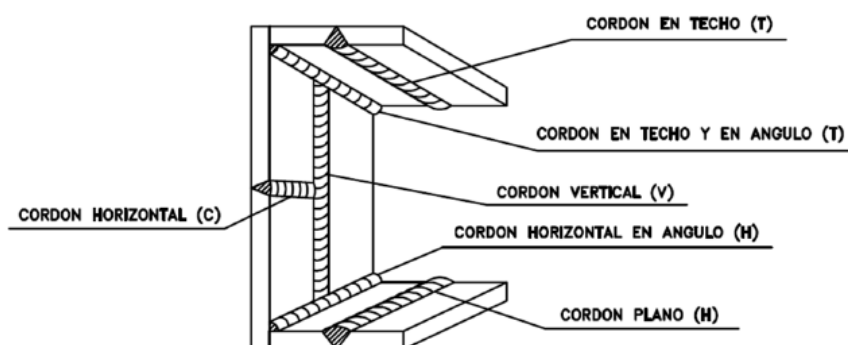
Clasificación del cordón de soldadura por la posición de este durante la operación a soldar.
